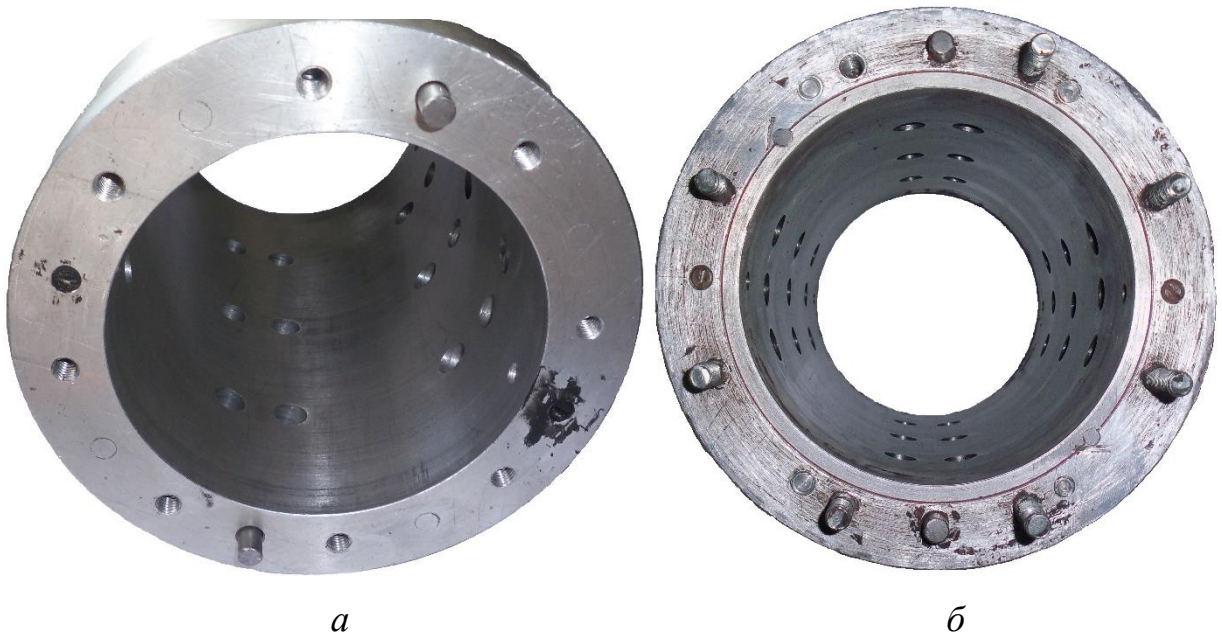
Варіанти виготовлення корпусу роторно-поршневого двигуна:
